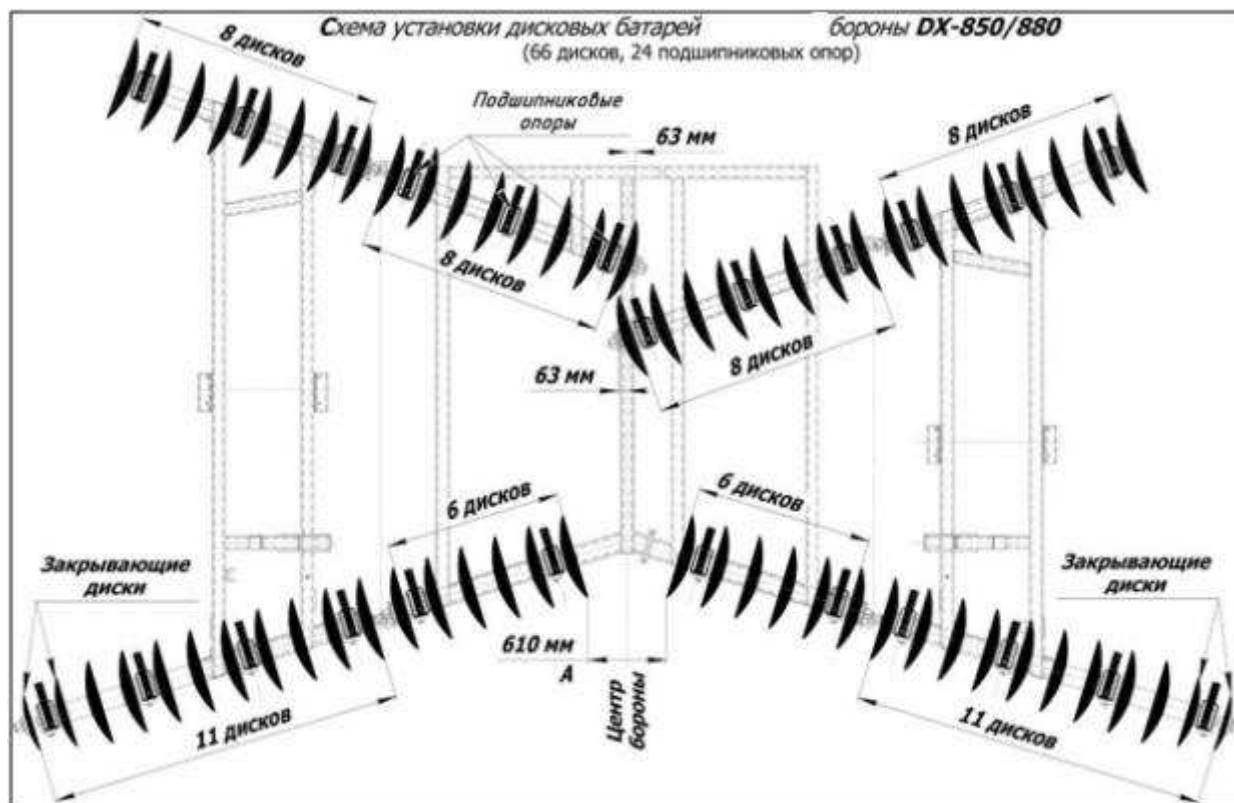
Схема установки дисковых батарей для бороны DX-850/880
